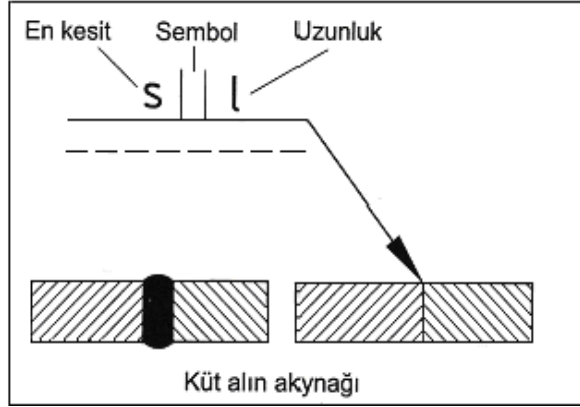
Kaynak yerlerinin sembollerle gösterilişi-1
